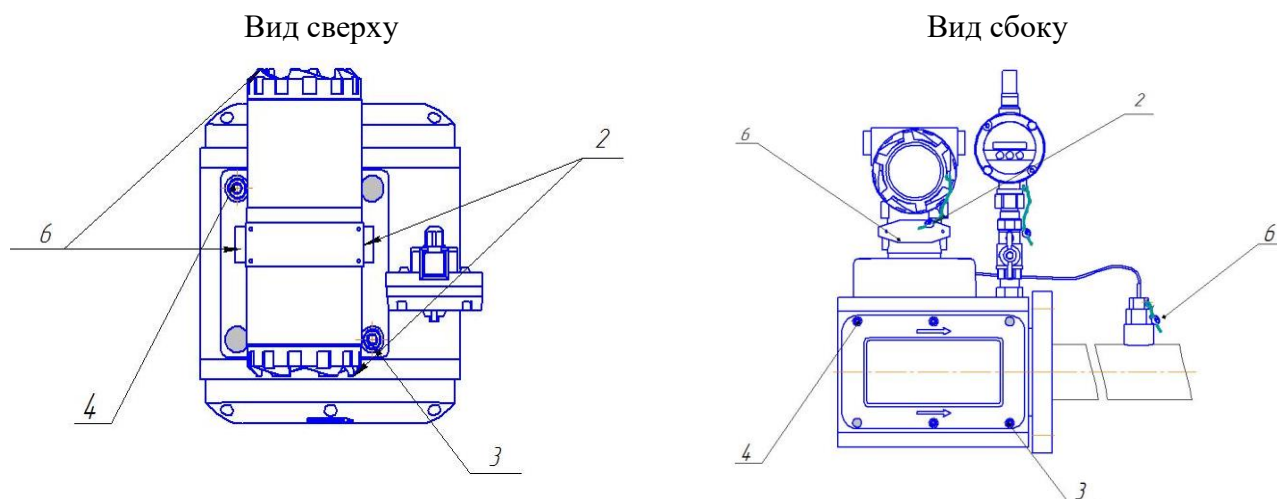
Корпус прямоугольного сечения с совмещенными защитными крышками
